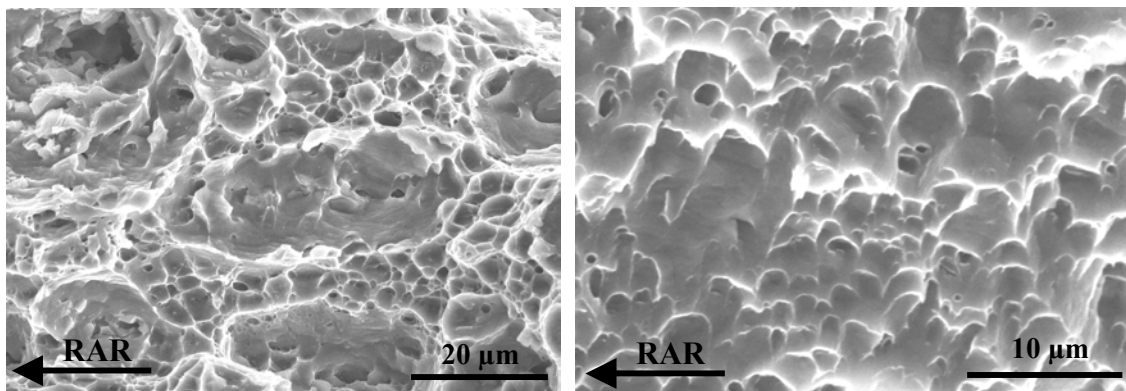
REM-Aufnahmen der Bruchflächen beim Dachriss
